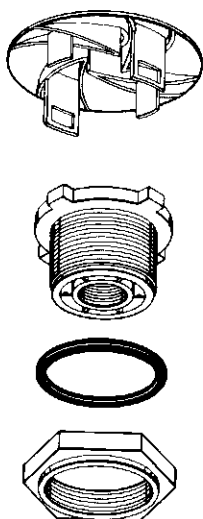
Anti-draaikolk kap voor montage bij de aansluiting voor de zuigleiding van de pomp (Delavan).
